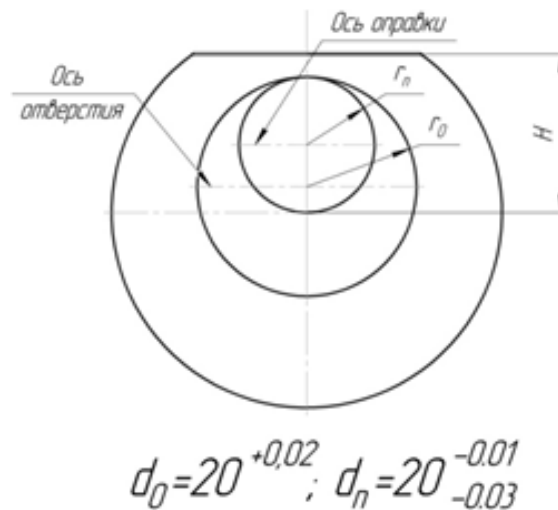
Схема установки детали в приспособлении к заданию 7
